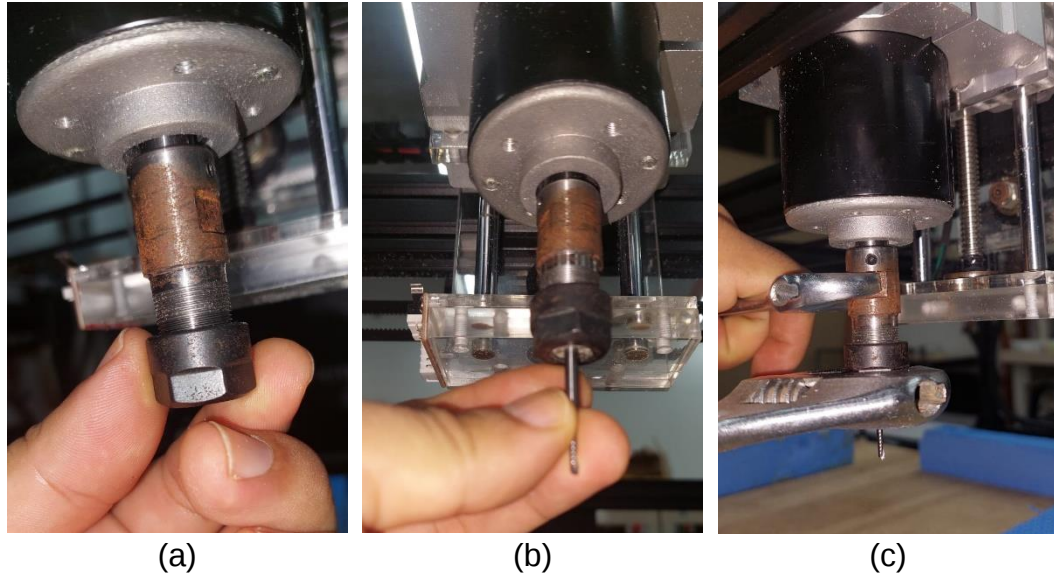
Fresa utilizada para realizar o ensaio de usinagem no bloco de espuma
